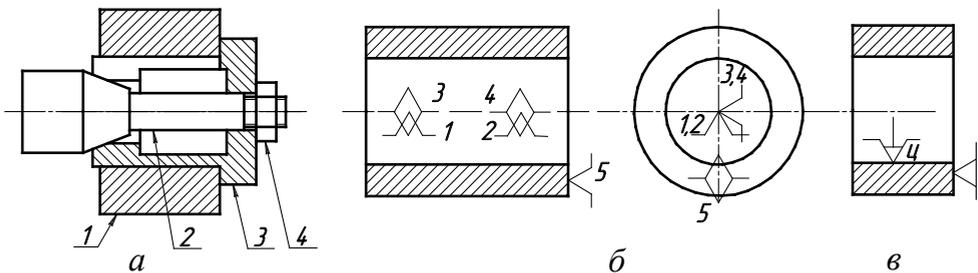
Установка длинной втулки на цанговой оправке:
